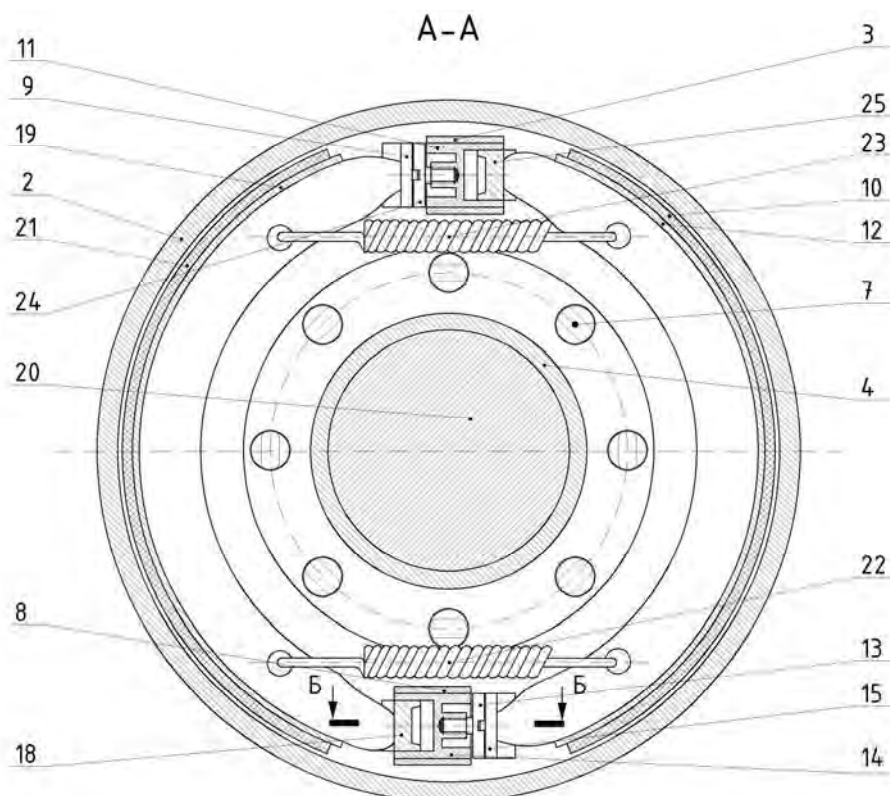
Разрез тормоза ведущего переднего моста колесного трактора с двумя первичными тормозными колодками: 2 – тормозной барабан; 3 – корпус; 4 – тормозной щит; 7 – болт; 8 – корпус; 9 – опора; 10 – фрикционная накладка; 11 – гидроцилиндр; 12 – тормозная колодка; 13 – винт регулировочный; 14 – гидроцилиндр; 15 – опора; 18 – поршень; 19 – тормозная колодка; 20 – полуось; 21 – фрикционная накладка; 22, 23 – пружина стяжная; 24 – винт регулировочный; 25 – поршень
